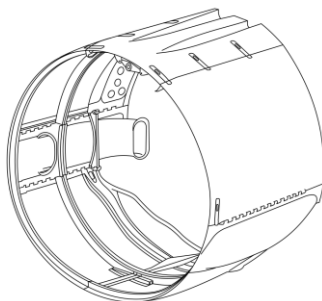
Обтекатель двигателя с внутренними каналами воздухозаборников
